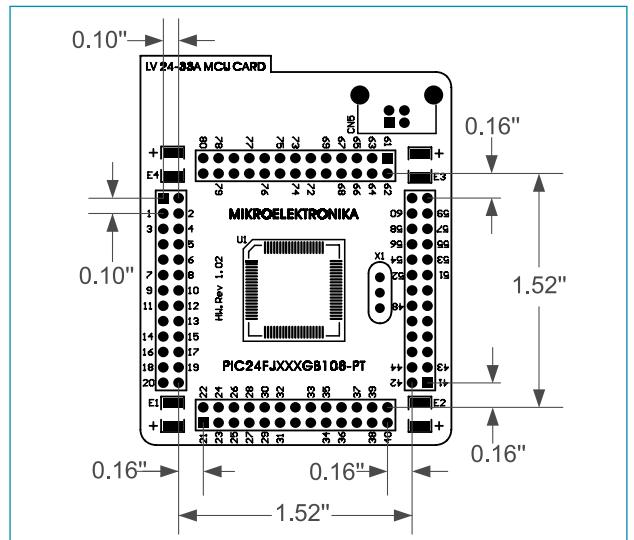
Dimensiones de la tarjeta MCU para la *MCU Card 16
